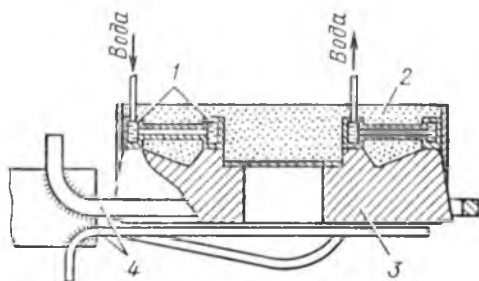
Подготовка штампа к проведению местного отпуска с помощью нагрева ТВЧ
